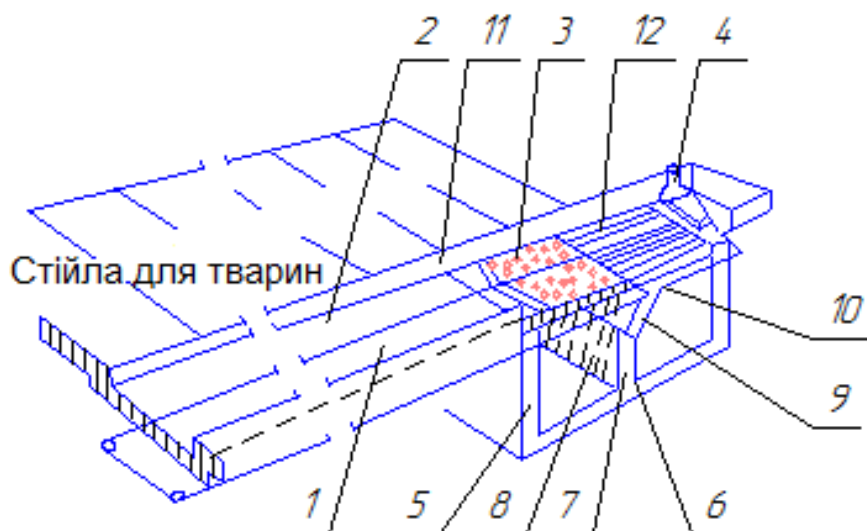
Конструкція пристрою для поділу гною на фракції: 1 – канал; 2 – ланцюг; 3 – скребок; 4 – привід; 5 – збірник для рідкої фракції; 6 – збірник твердої фракції; 7 – перегородка; 8 – щит; 9 – важіль; 10 – кулачок; 11 – похила частина; 12 – решітка
